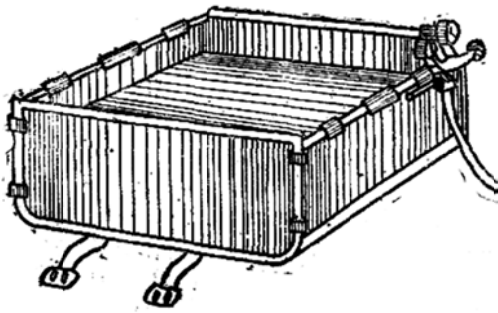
Ванна для проверки радиаторов и камер в рабочем положении
